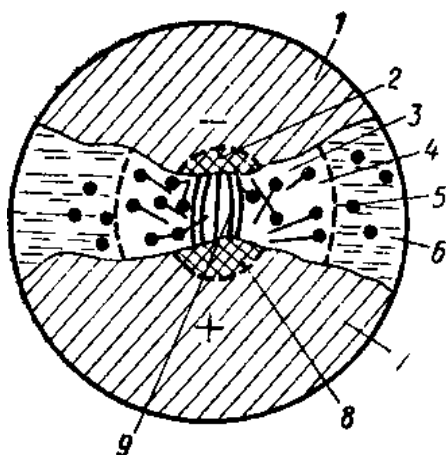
Мікрорельєф поверхні та схема розряду між електродами: 1 – катод; 2 – мікропорція металу, виплавлена на поверхні катода; 3 – газовий пухирець; 4 – розплавлені частинки металу; 5 – частинки металу, застигли в робочій рідині; 6 – робоча рідина; 7 – анод; 8 – мікропорція металу, виплавлена на поверхні анода; 9 – канал розряду
